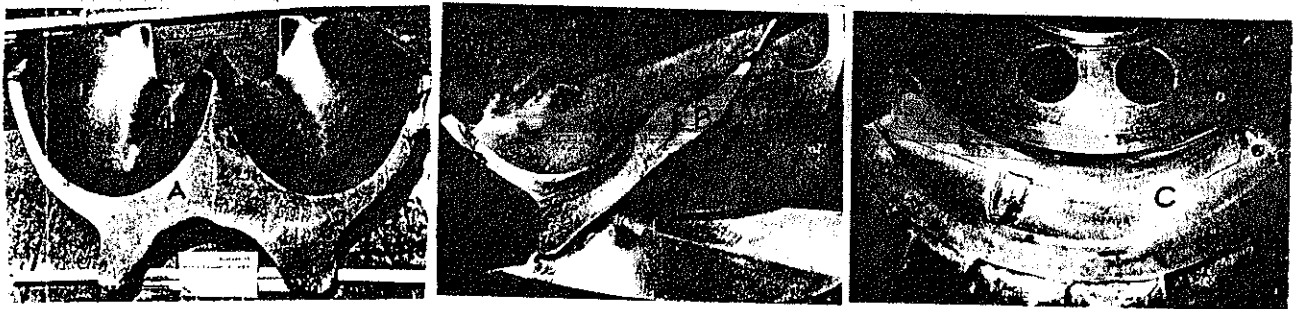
A: Cara fracturada de un cangilón dañado. La fisura se inició en la zona de soldadura.
